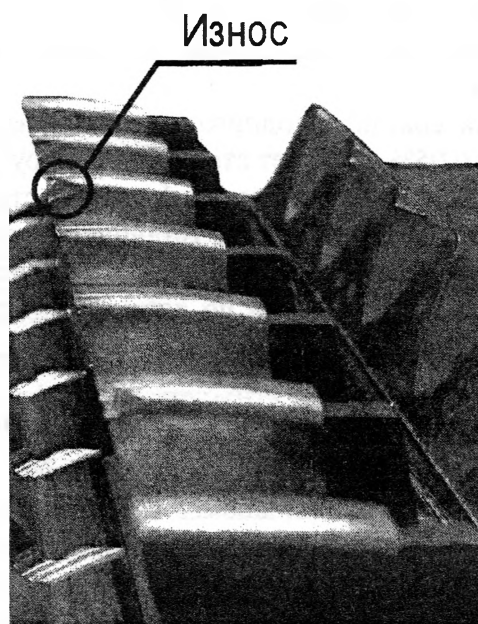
Износ зубьев червячной фрезы по задней поверхности
